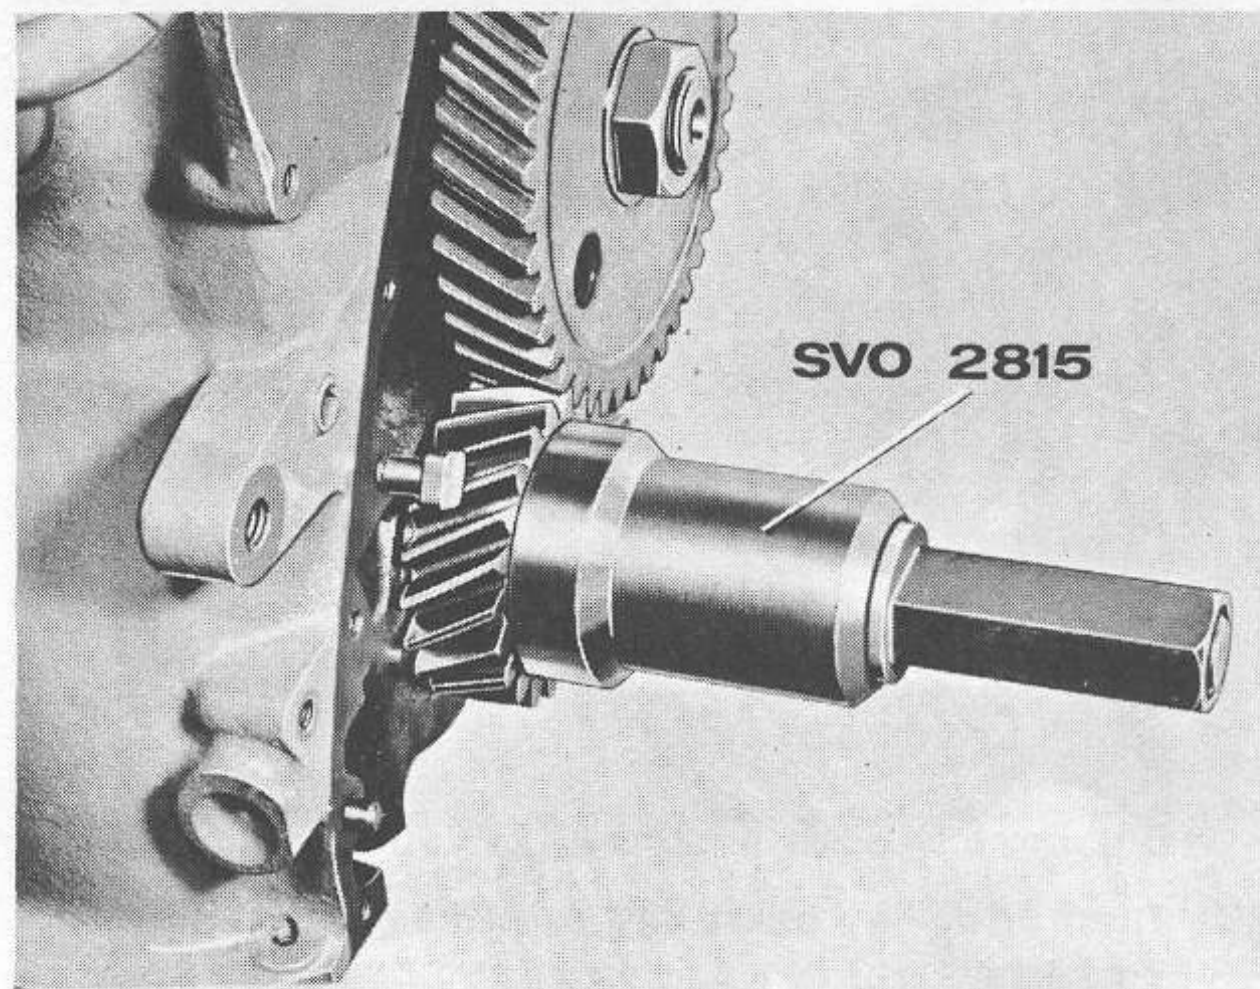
Montering av vevaxeldrev (6-cyl. motor)
